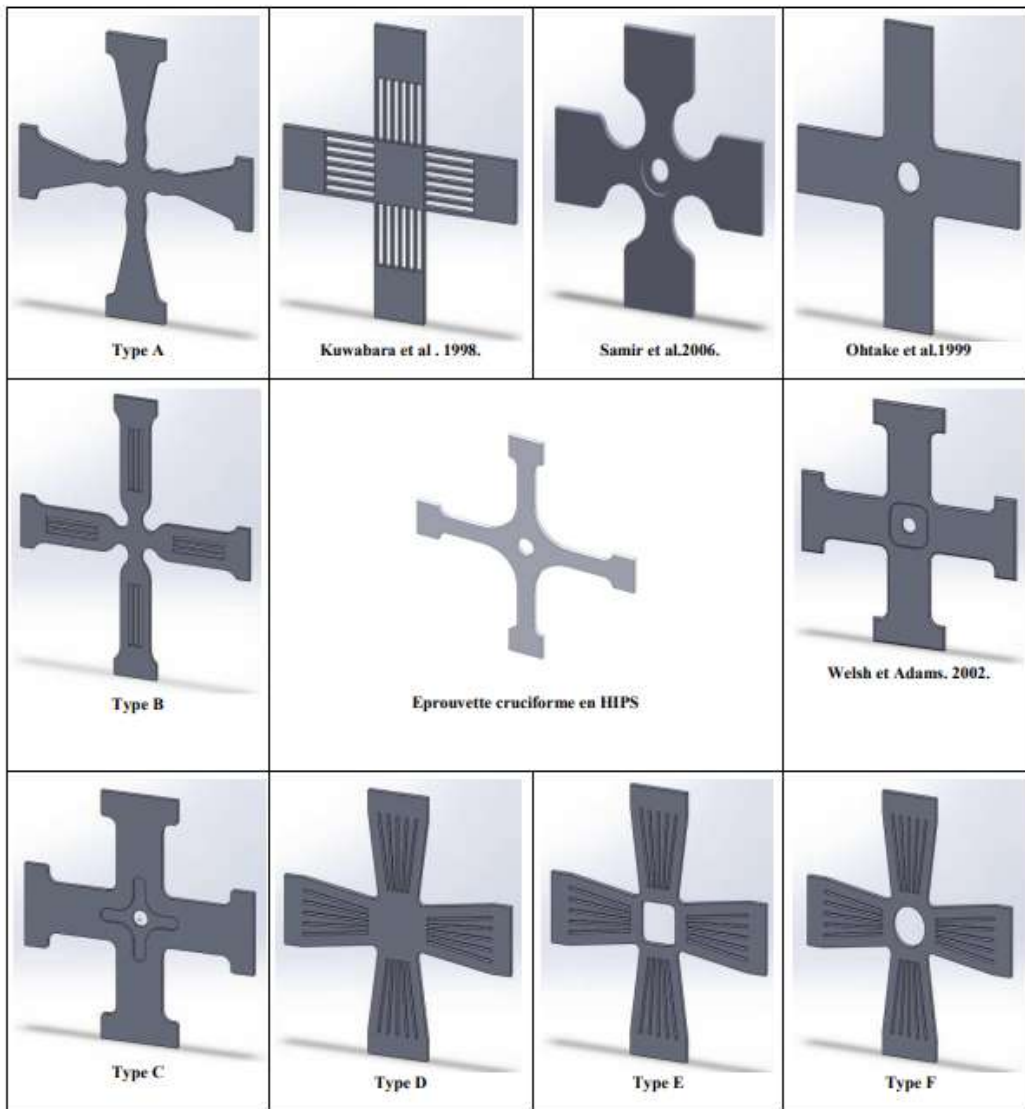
Formes des éprouvettes fréquemment utilisées dans le champ de recherche[17]
